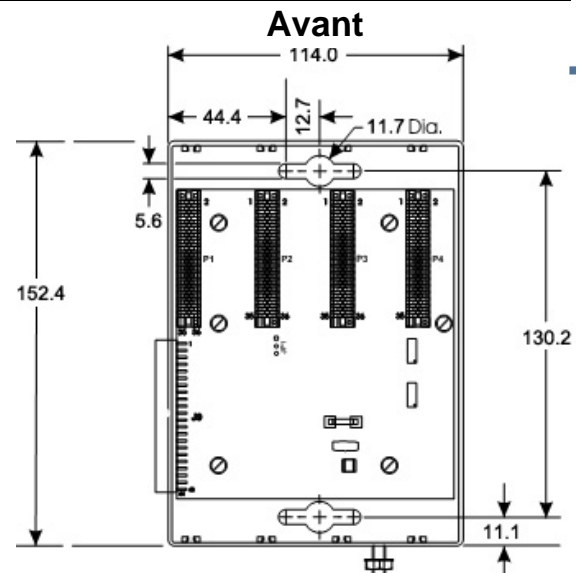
Dimensions du boîtier d'expansion à 4 emplacements ControlWave Micro (en millimètres)
